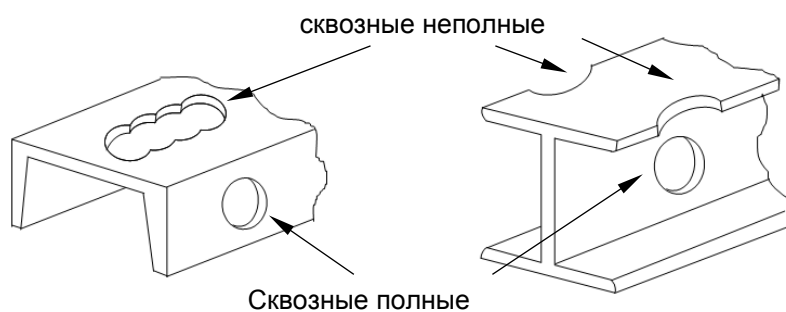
Типы отверстий, выполняемых кольцевыми фрезами
